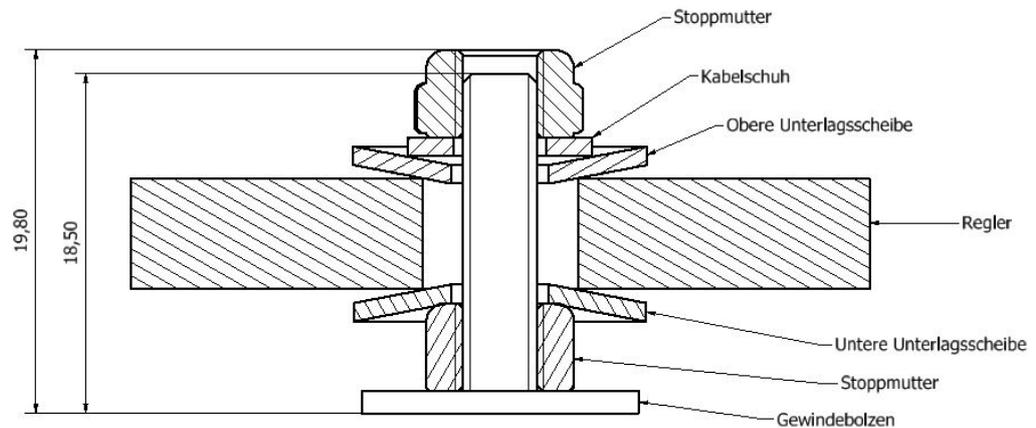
Aufbau des Gewindebolzens für die Befestigung des Reglergleichrichters und des Massekabels (Kabelschuh)
